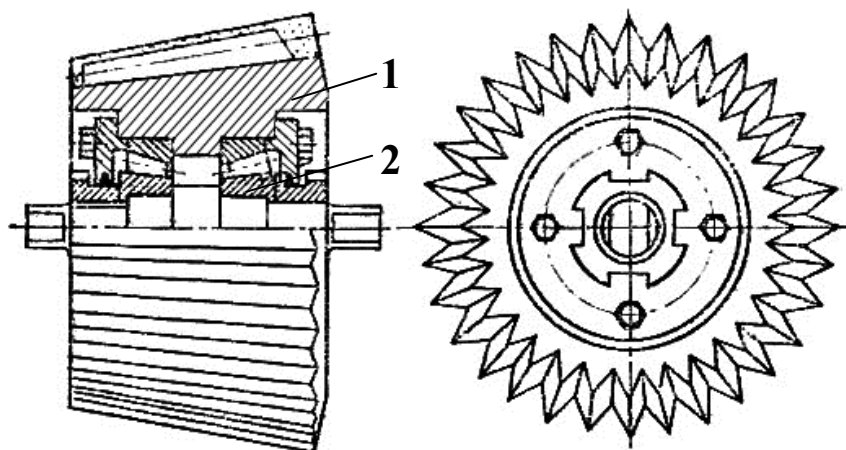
Зубчатая шарошка: 1 – корпус; 2 – подшипниковая опора
